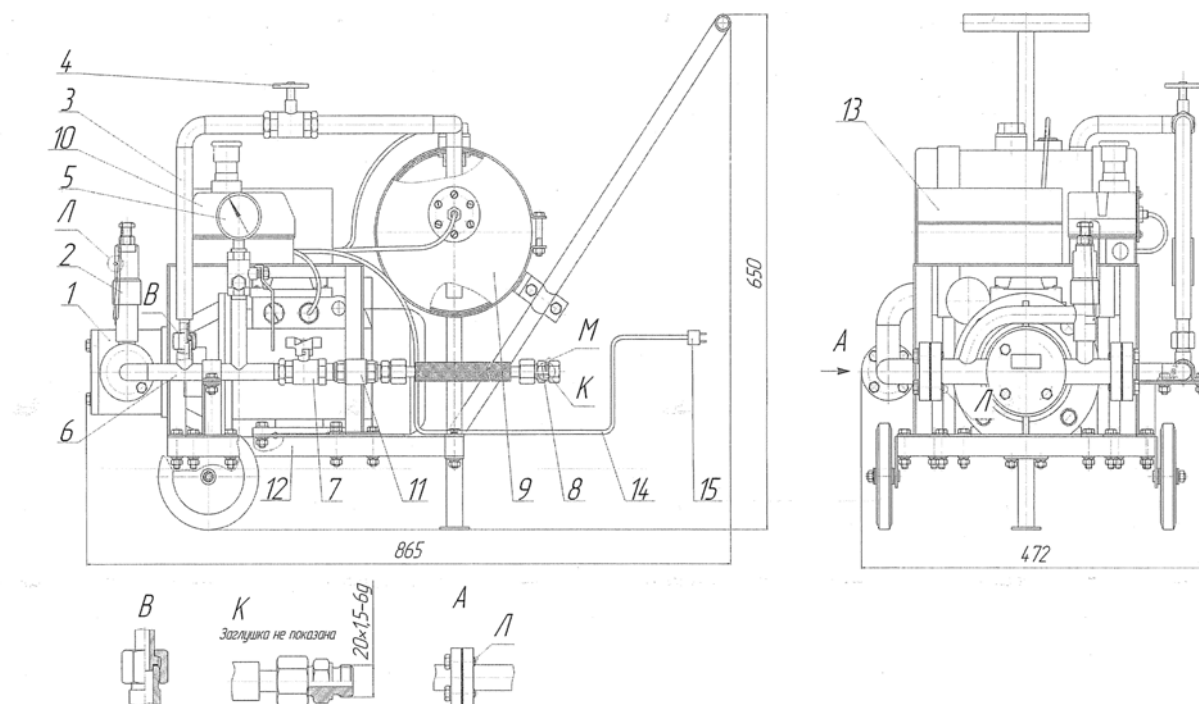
Габаритный чертеж маслоочистительной установки JEV50AP001
